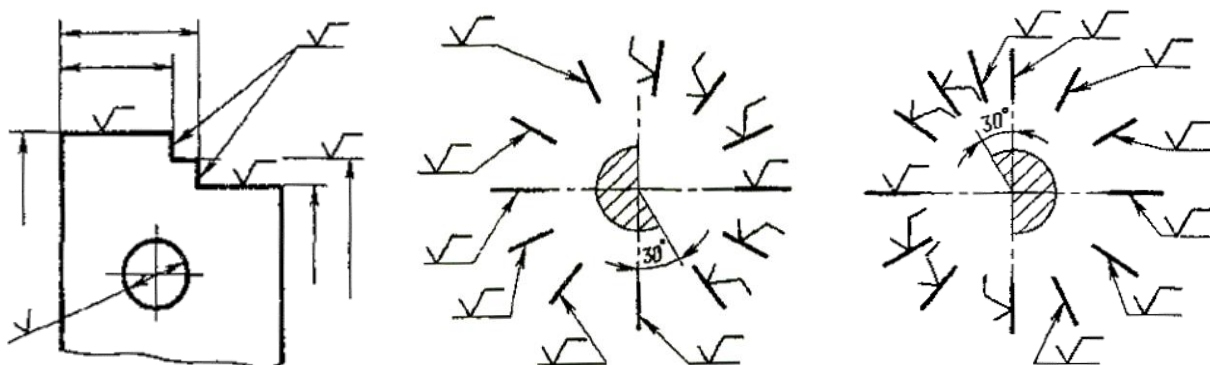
Обозначения шероховатости поверхности, в которых знак имеет полку
